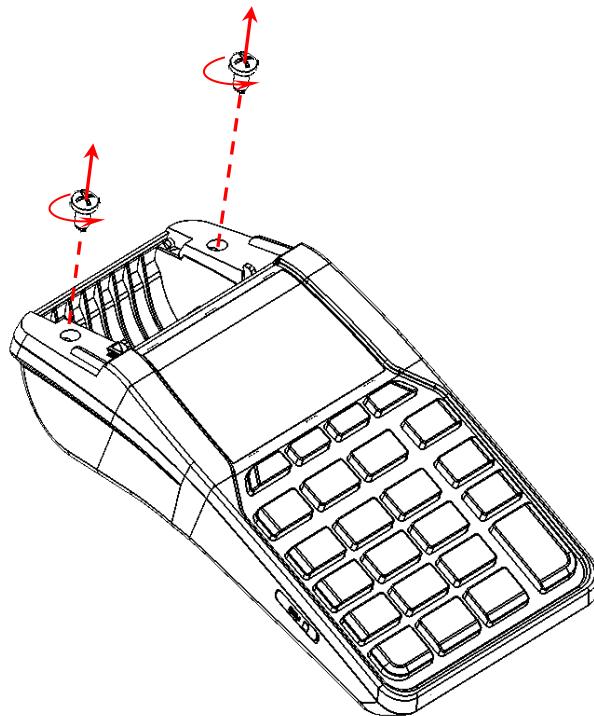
Винты крепления в верхней части корпуса ККТ
